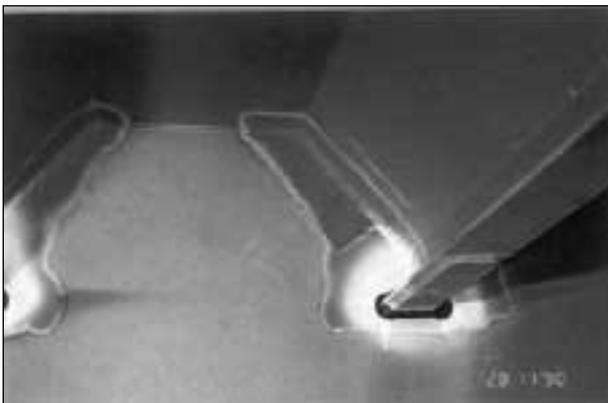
Rissuntersuchung der Schweißnähte mit dem Farbeindringverfahren
